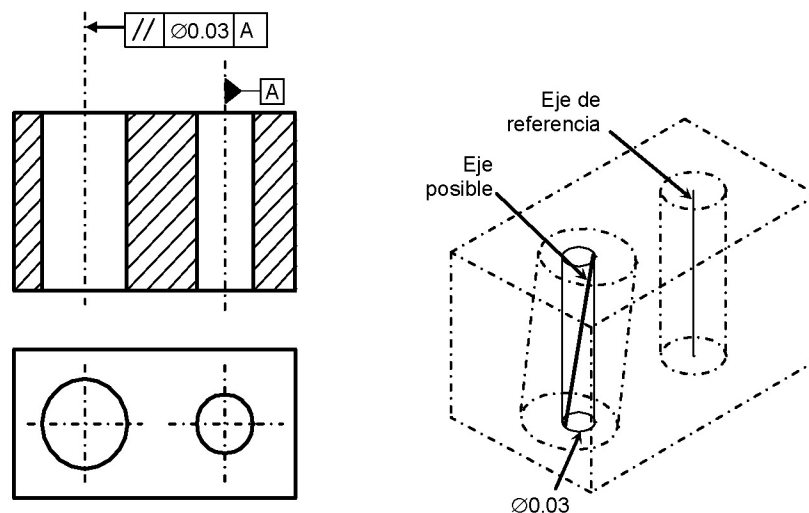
Tolerancia de paralelismo con zona de tolerancia cilíndrica
